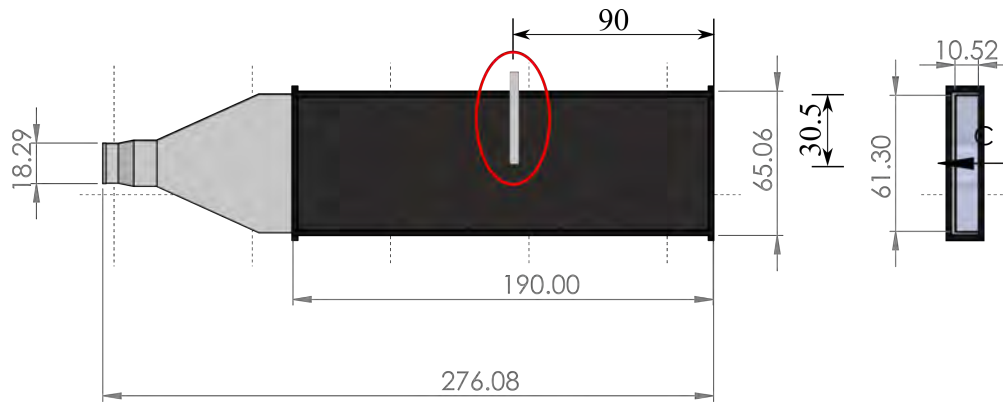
Diagrama esquemático del CSA en vista de planta y frontal
